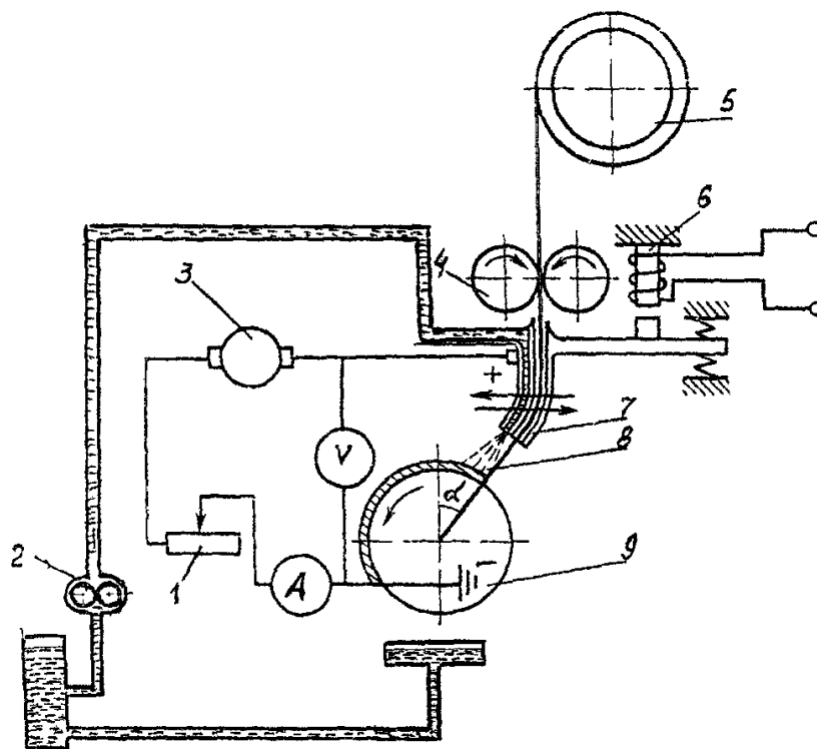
Принципова схема пристрою для автоматичного вібродугового наплавлення
